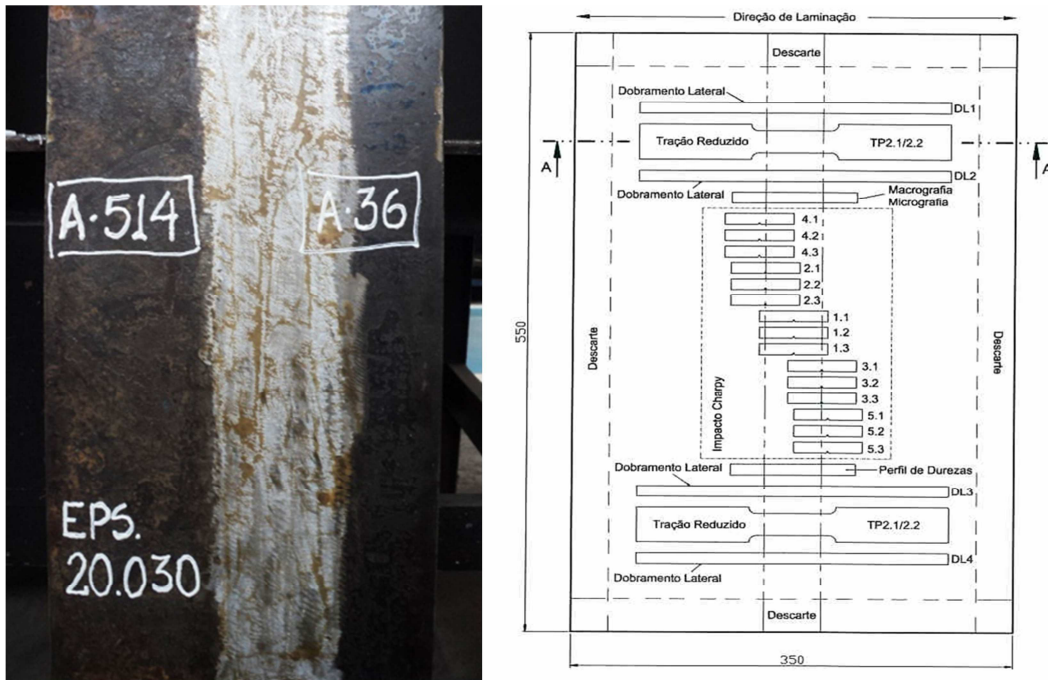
(À esq.) Peças de testes PT-01/PT-02 soldada e com o reforço de solda removido para posterior inspeção por ultra-som. (À dir.) Locais de remoção dos corpos de prova nas peças de testes PT-04/PT-05 conforme Figura 4.10 da norma AWS D1.1/D1.1M:2010 [5].
